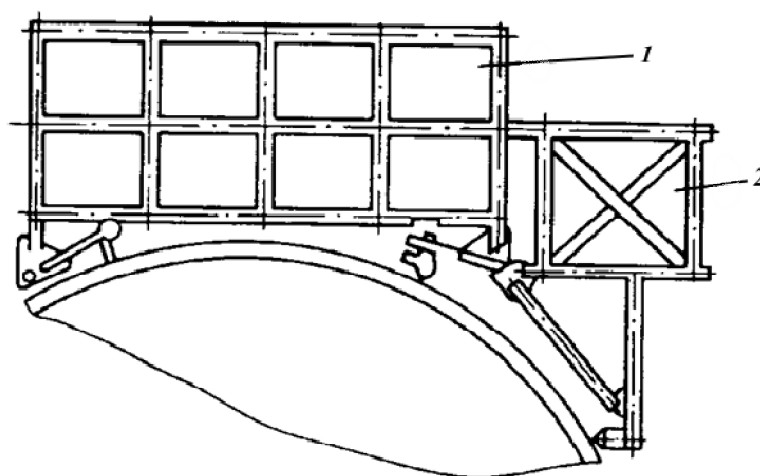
Площадка для сварки стыка обечаек:
